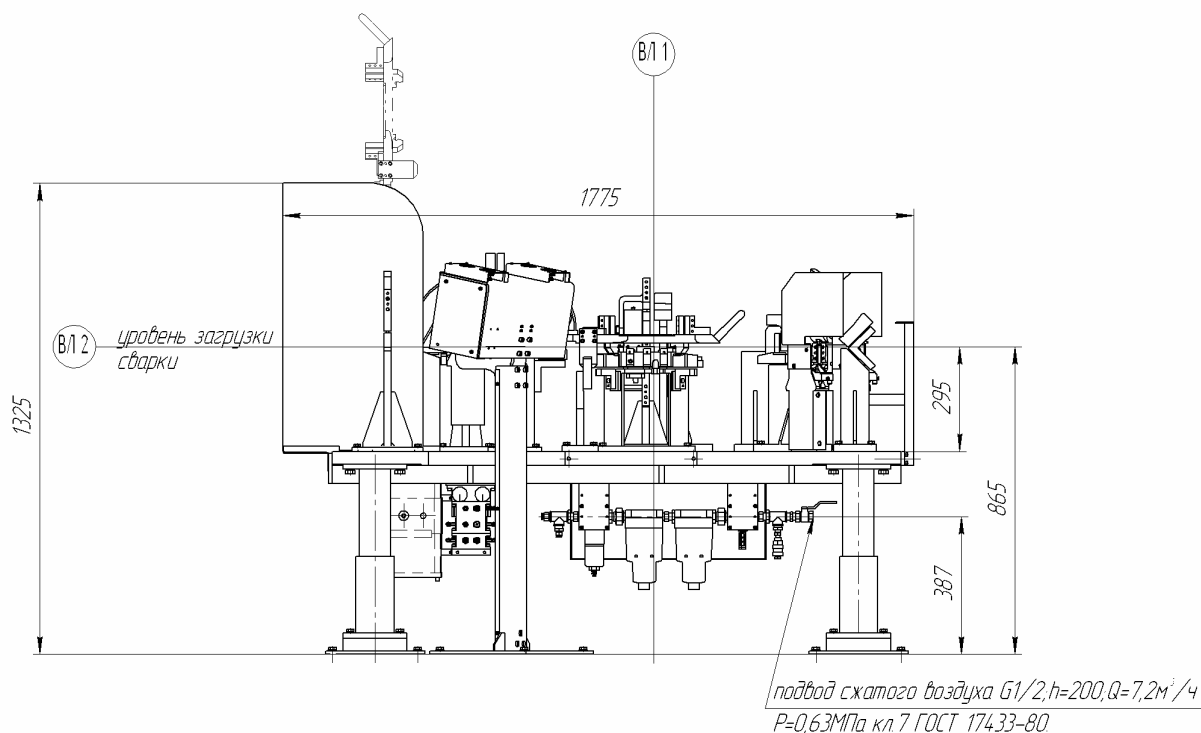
Приспособление для сборки и сварки
